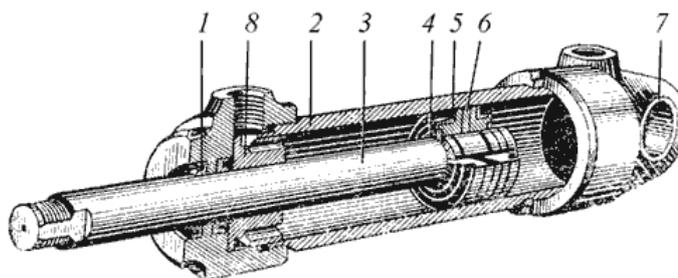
Гидроцилиндр: 1 - грязесъемник; 2 - гильза; 3 - шток; 4 - опорное кольцо; 5 - манжета; 6 - поршень; 7 - проушина; 8 - грядбукса
